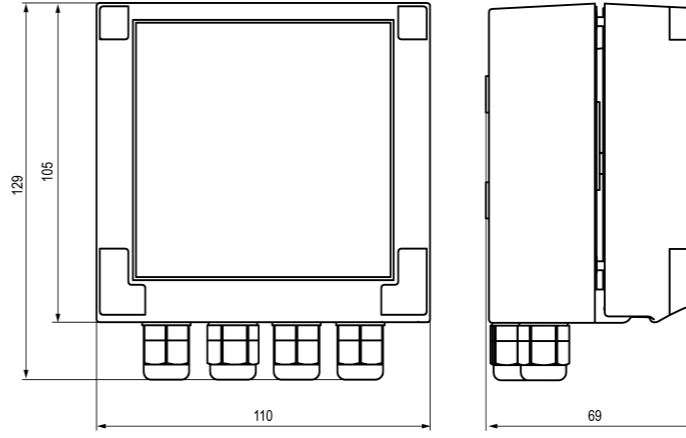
Габаритные размеры прибора в корпусе Н
